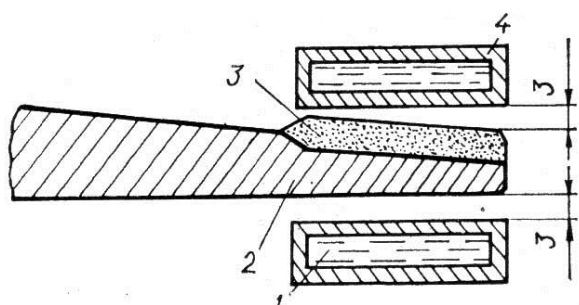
Схема індукційного наплавлення порошкоподібних твердих сплавів:
